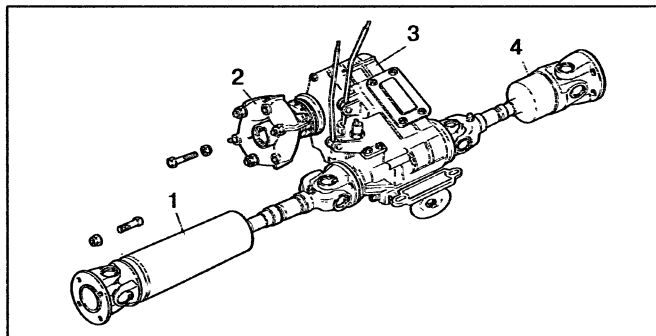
Карданная передача в сборе: 1 – передний карданный вал; 2 – промежуточный карданный вал; 3 – раздаточная коробка; 4 – задний карданный вал
